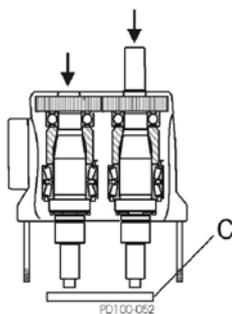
Wellen aus dem Getriebegehäuse drücken
